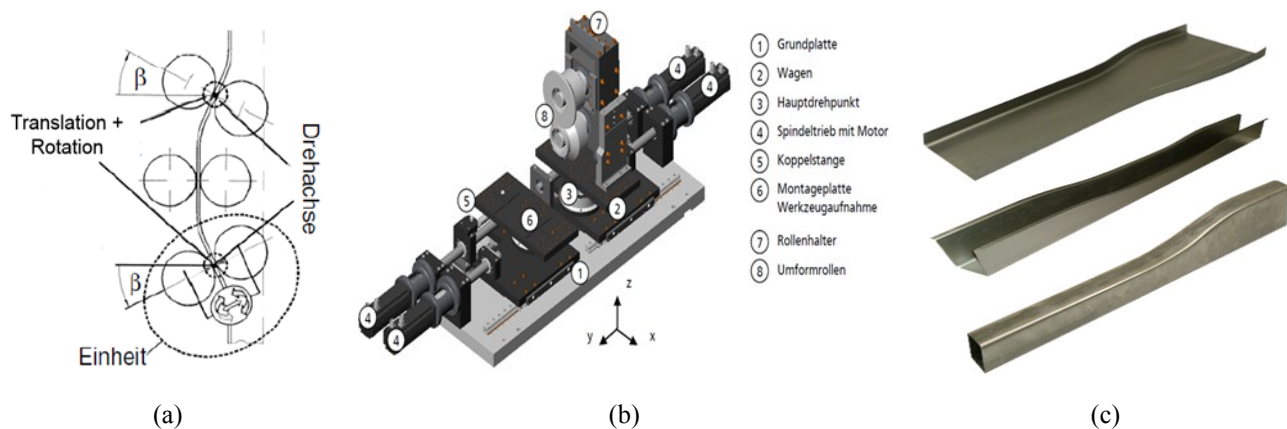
Funktionsprinzip flexibles Walzprofilieren [4] (a); Gerüstaufbau [5] (b); Beispiel Bauteile [6] (c)
